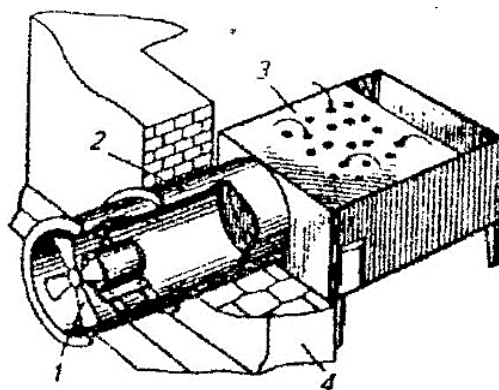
Вытяжная вентиляция на рабочем месте сварщика: 1 – Вентилятор, 2 – вытяжная труба, 3 – стол сварщика, 4 – стена
